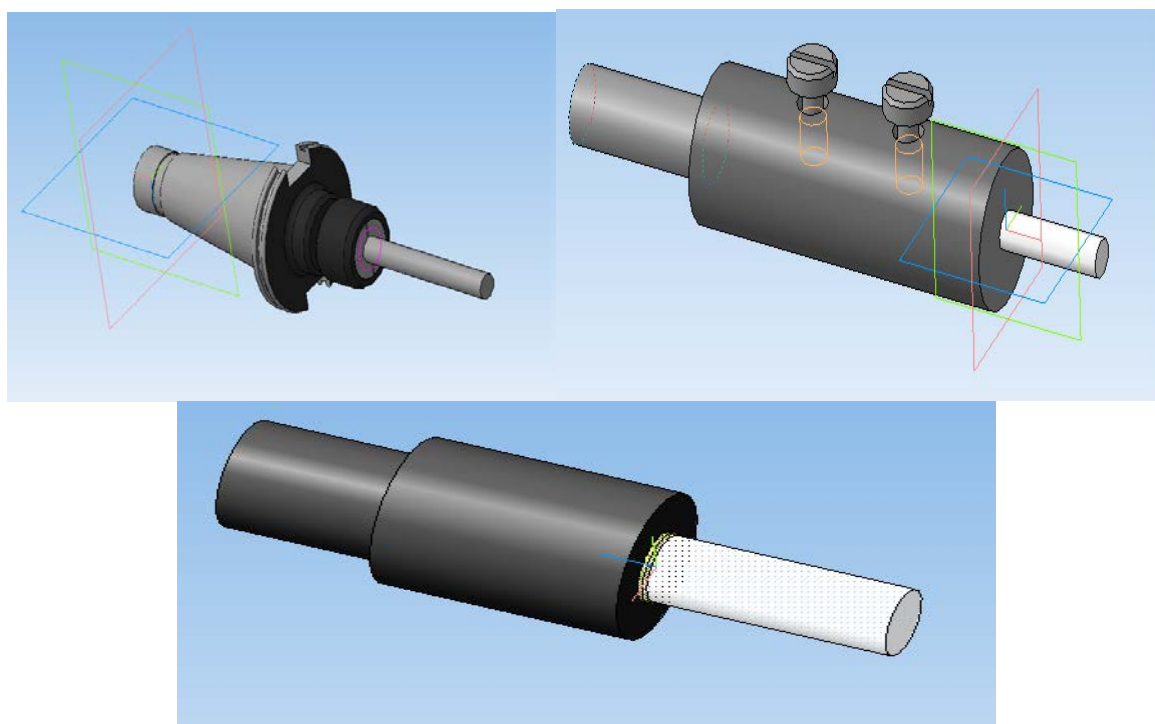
Способы закрепления и оценка напряжений заготовки, при ее обработке
